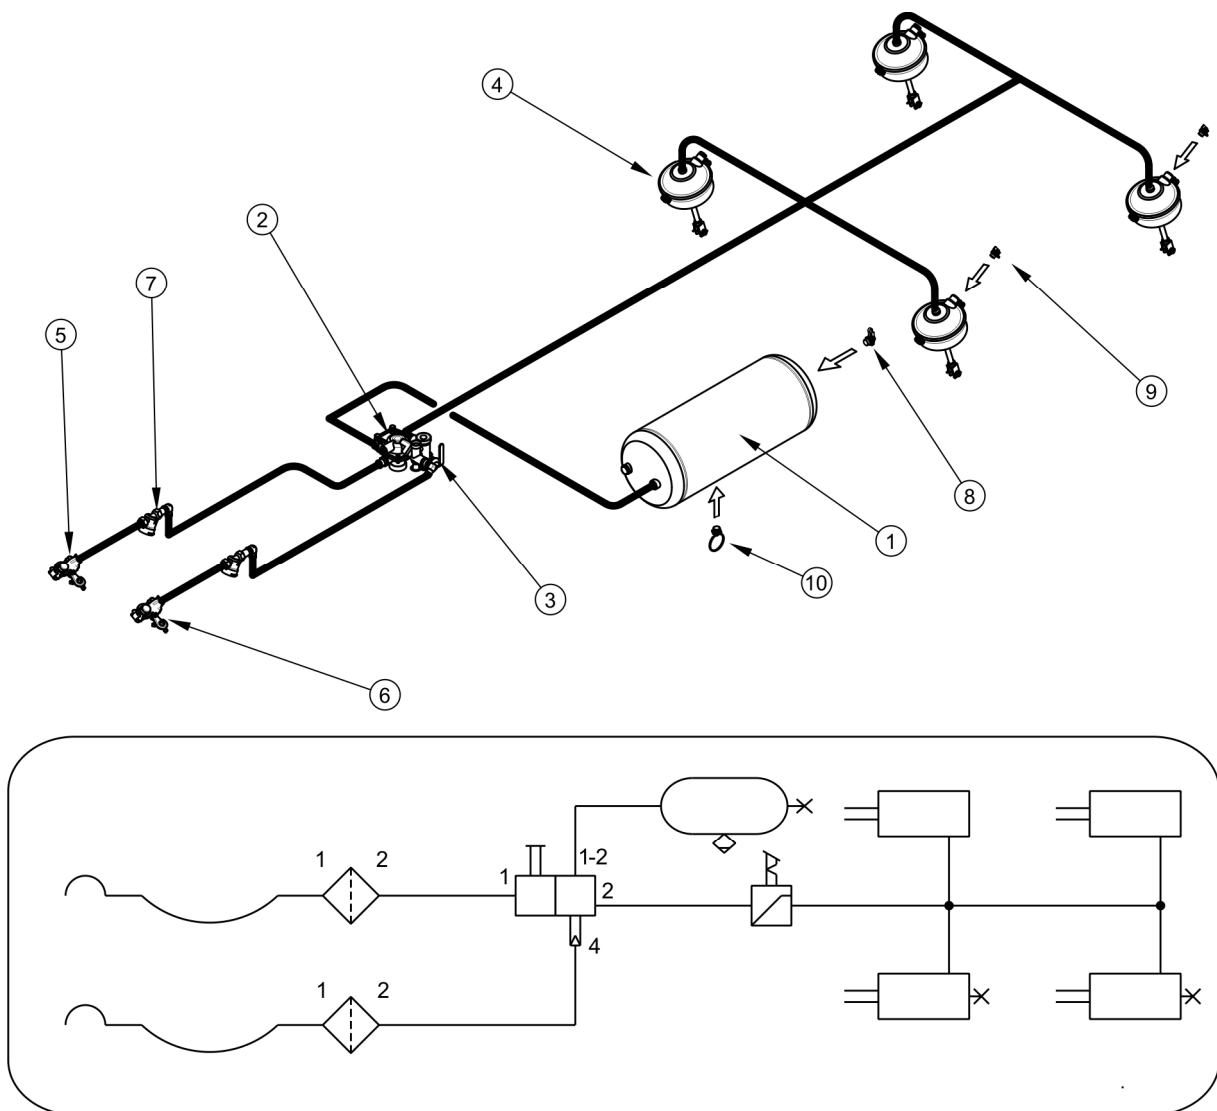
Konstrukce a schéma hydraulické brzdové instalace
